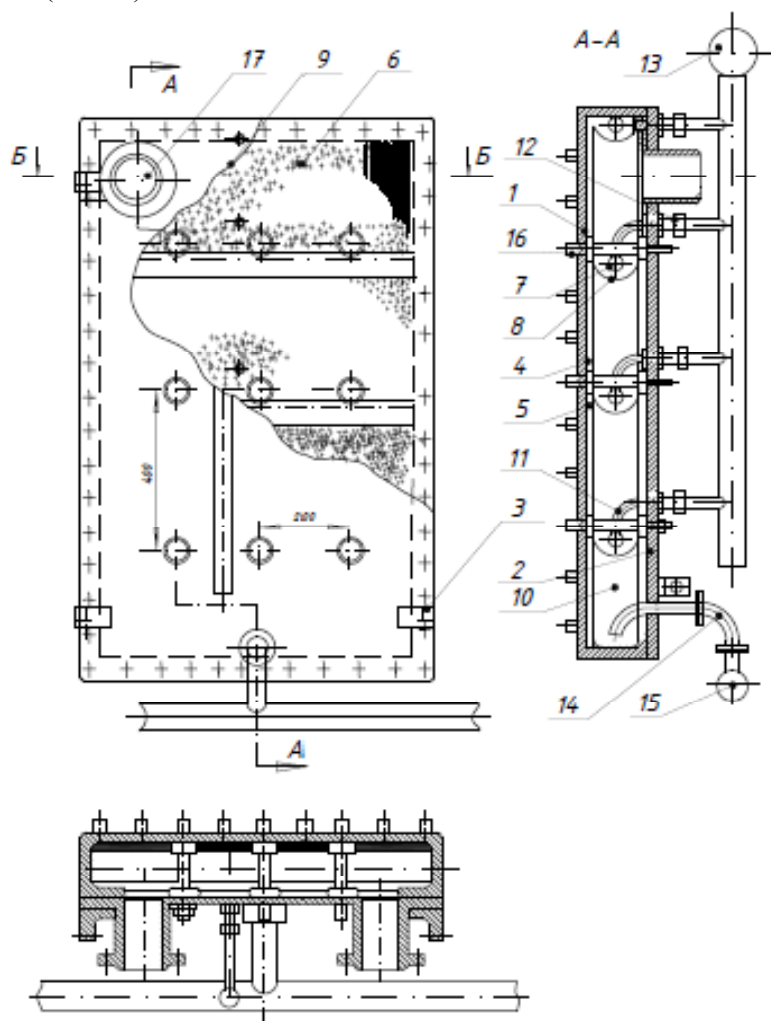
Схема охлаждения кессона капиллярно-пористой системы с распорками: 1 - корпус; 2 - крышка; 3 - болт; 4 - стенка; 5 - капиллярно-пористая структура; 6 - пластина; 7 - артерия; 8 - корытце; 9 - отверстие; 10 - канал; 11, 17 - патрубок; 12 - труба; 13, 15 - коллектор; 14 - сифон; 16 - распорки
